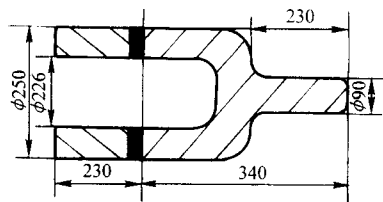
压力阀套焊接结构及尺寸
